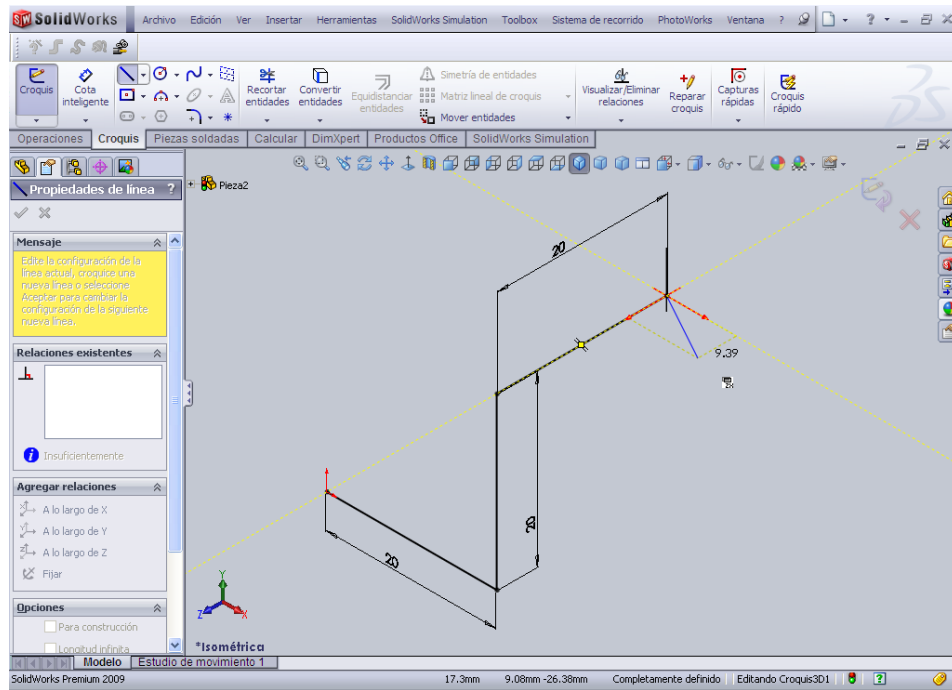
Croquis 3D en construcción de la estructura tubular
